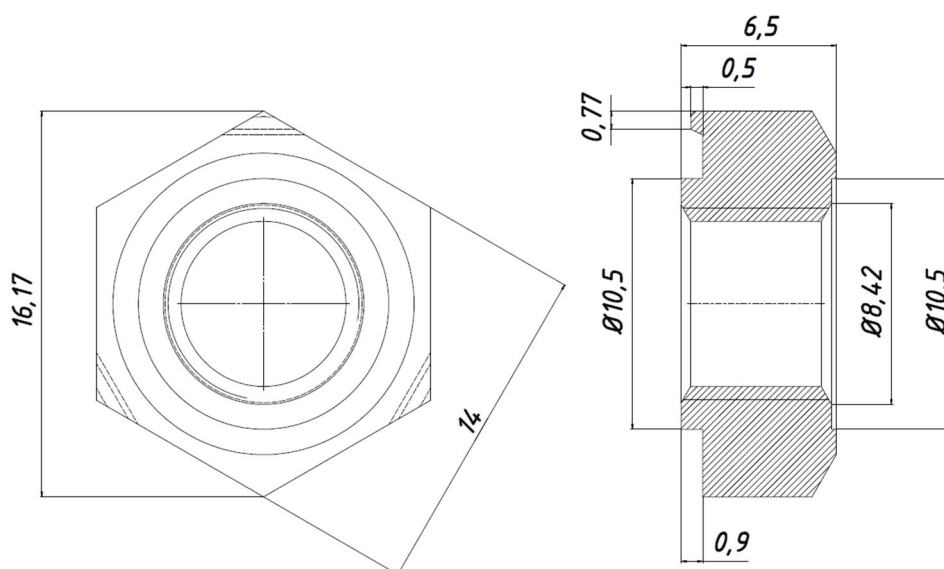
Размеры приварной гайки 1/40988/00.
